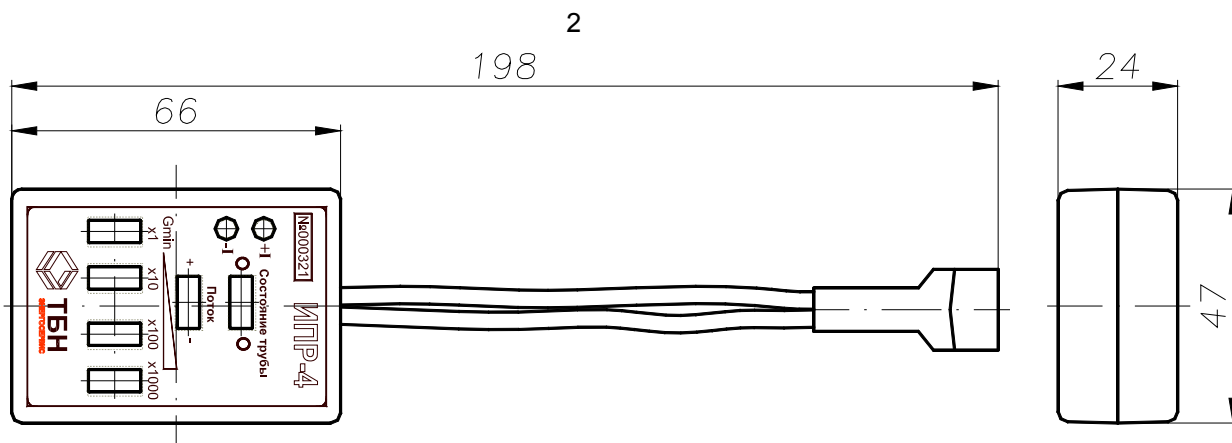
Внешний вид и габариты имитатора преобразователя расхода
